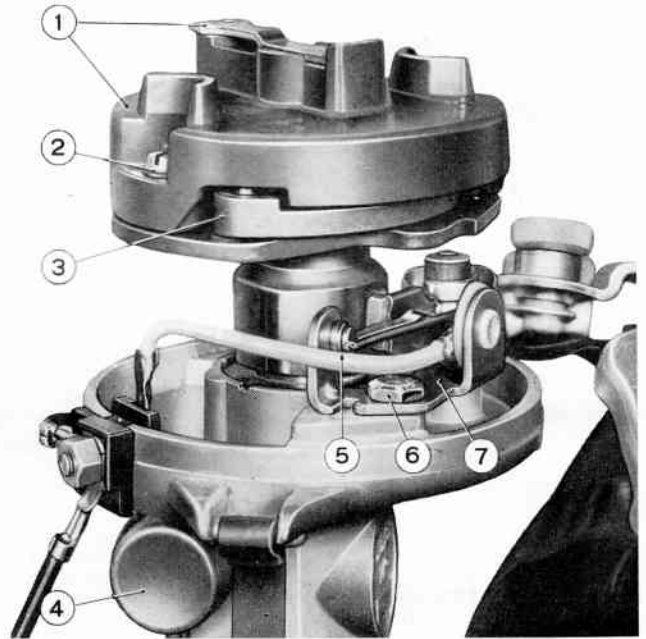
Zündverteiler am Motor, bei abgenommener Kappe. 1. Verteilerlaufstück - 2. Befestigungsschraube des Verteilerlaufstücks - 3. Fliehkewichte - 4. Kondensator - 5. Kontakte - 6. Schraube zur Befestigung und Einstellung der Festkontakplatte - 7. Kontaktplatte.
